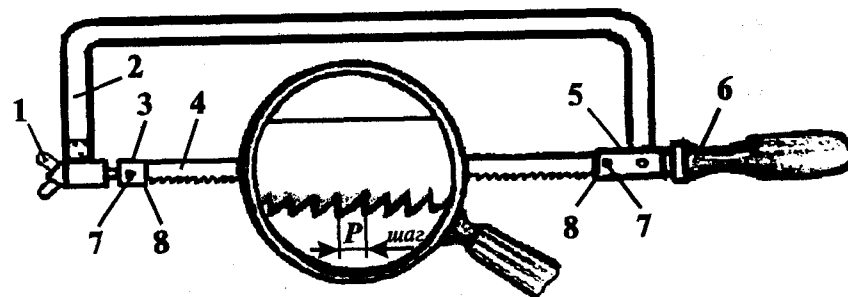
Ручная ножовка: 1 — гайка; 2 — рамка; 3 — подвижная головка; 4 — ножовочное полотно; 5 — неподвижная головка; 6 — хвостовик с ручкой; 7 — штифты; 8 — прорези
